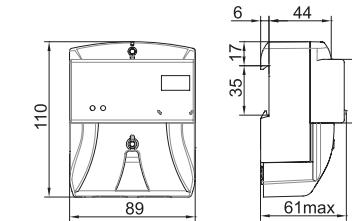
Габаритные и присоединительные размеры счётов габарита корпуса 5.
